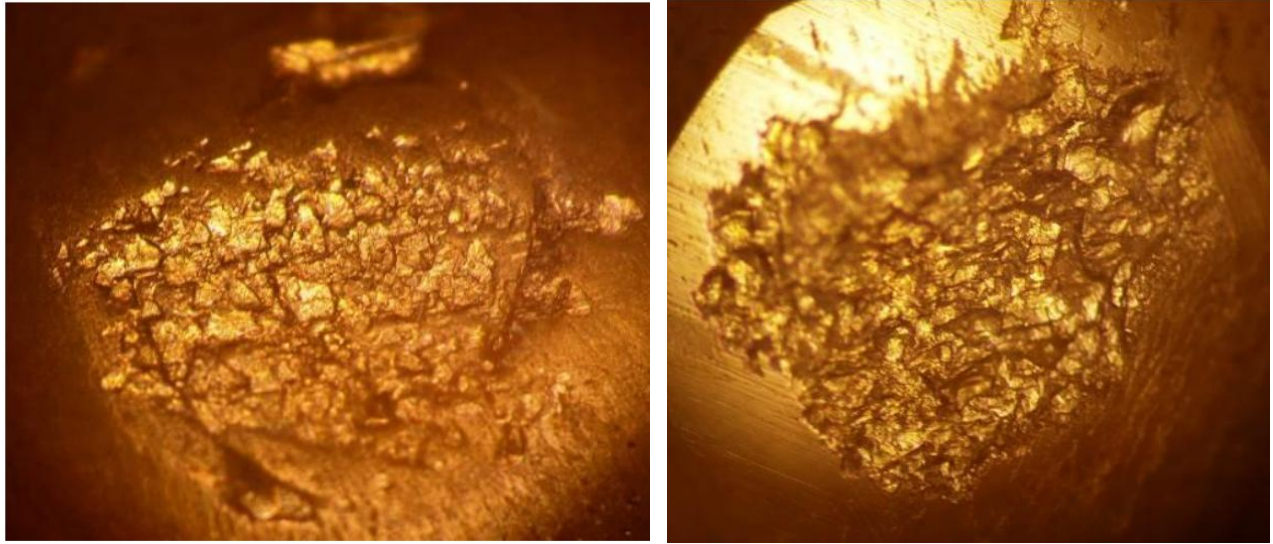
Збільшені фрагменти ділянок робочої поверхні інструменту після ультразвукового вигладжування
